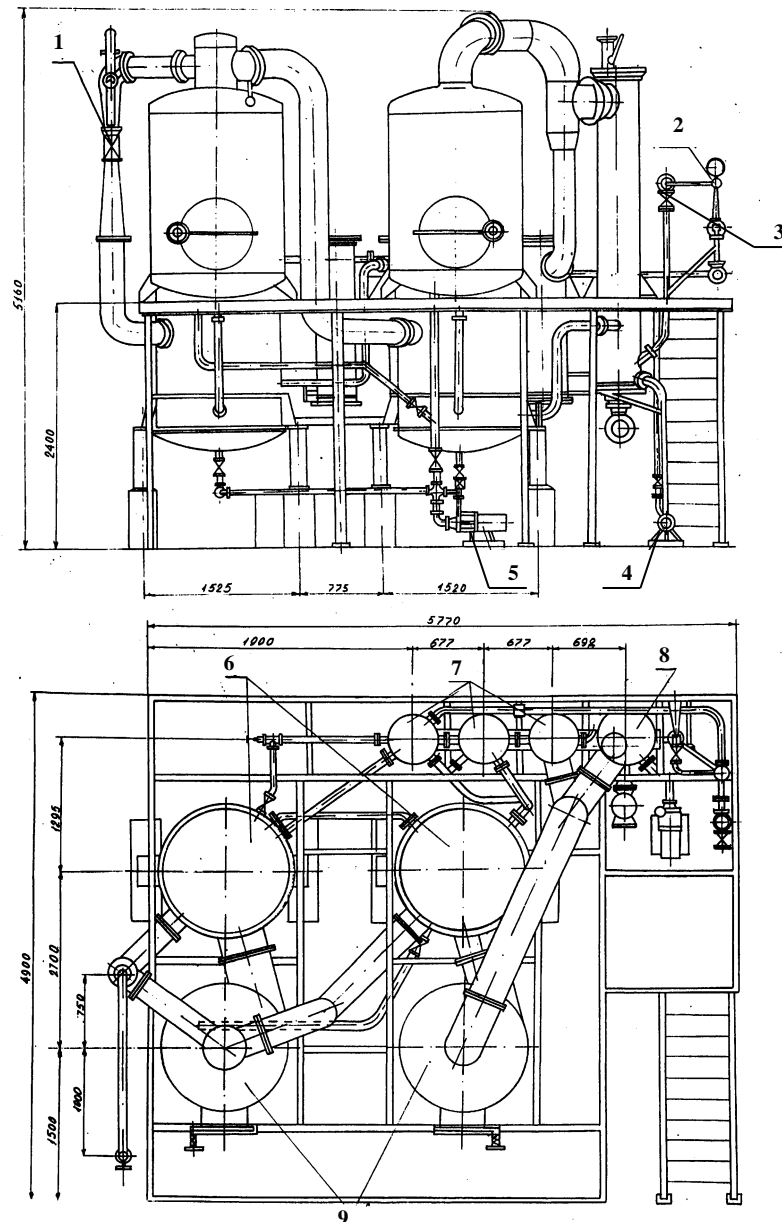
Загальний вид вакуум-випарювальної установки Віганд-4000
